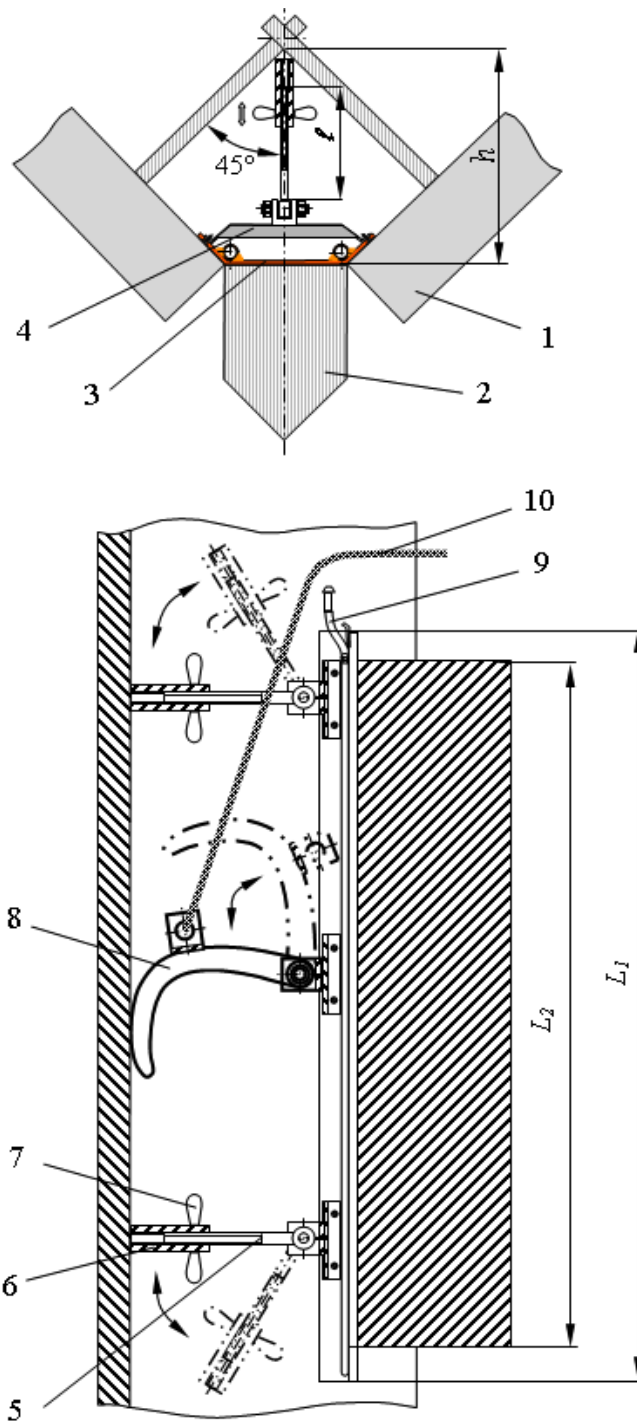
Схема кріплення пристрою для формування зварного шва на будівельному колоні: 1– фрагмент пояса колони; 2 – елемент посилення колони; 3 – формувальна накладка, охолоджувана водою; 4 – кронштейн; 5 – гвинт; 6 – втулка; 7 – рукоятка; 8 – упор; 9 – мідна трубка; 10 – тяга.
